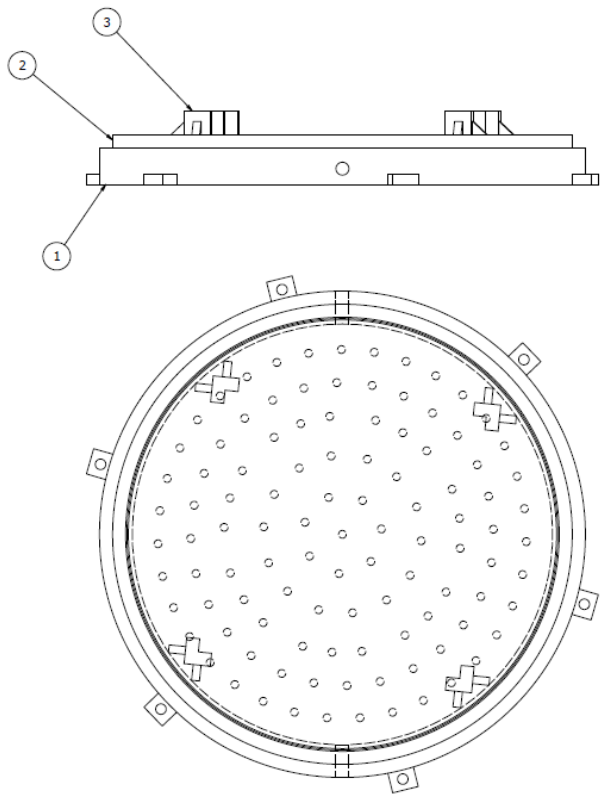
Ensamblaje preliminar banco de pruebas plano.
